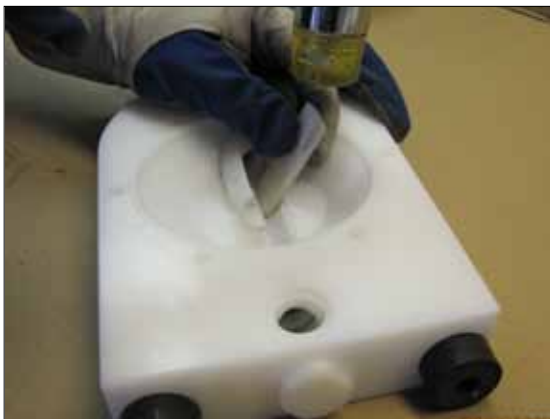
Um das Distanzstück (19) zu entfernen, nehmen Sie ein Stück Kunststoff und schlagen vorsichtig mit einem Hammer um es zu drehen.
